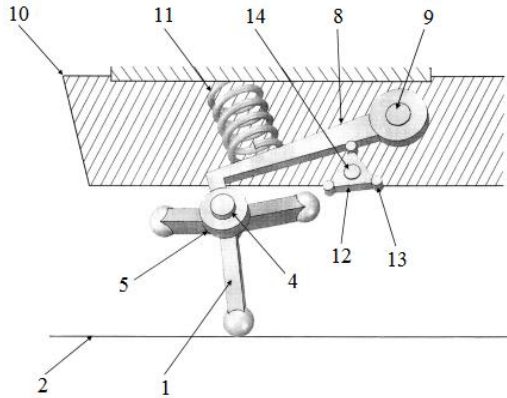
Компенсатор коливань в зборі: 1 – опори; 2 – опорна поверхня; 4 – вал; 5 – маточина; 8 – важіль; 9 – нерухома вісь; 10 – рама; 11 – пружина; 12 – кулачковий механізм; 13 – ролики; 14 – вал
